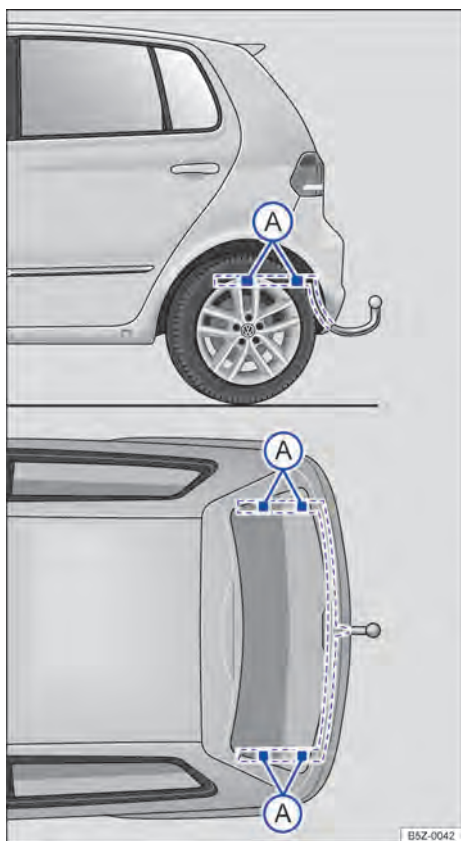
Pontos de fixação para instalar um dispositivo de reboque posteriormente.
